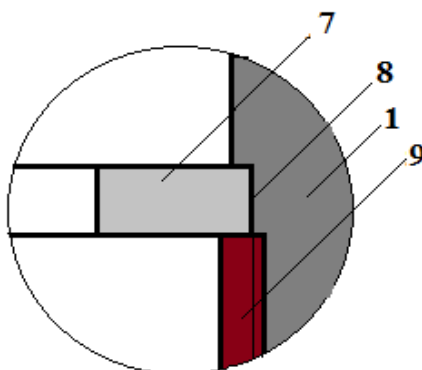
Схема кріплення диска штопорною втулкою у виточці корпусу
